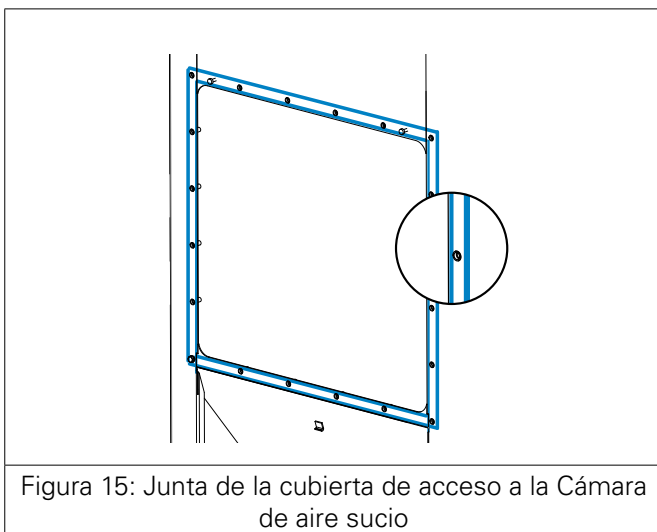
Junta de la cubierta de acceso a la Cámara de aire sucio
